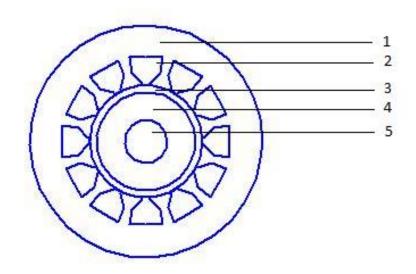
Поперечный разрез синхронного генератора: 1-ярмо статора вал, 2-обмотка статора, 3-воздушный зазор, 4- магниты, 5-вал.
